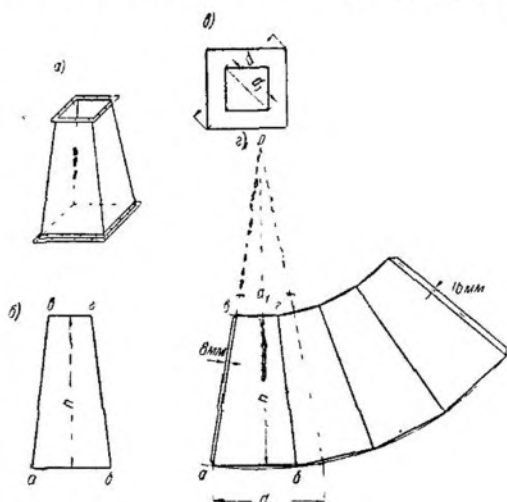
Развертка перехода с квадратного на квадратное сечение
